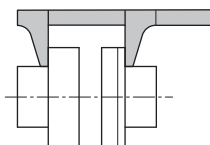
Проверка осевой выверки при помощи штангенциркуля
